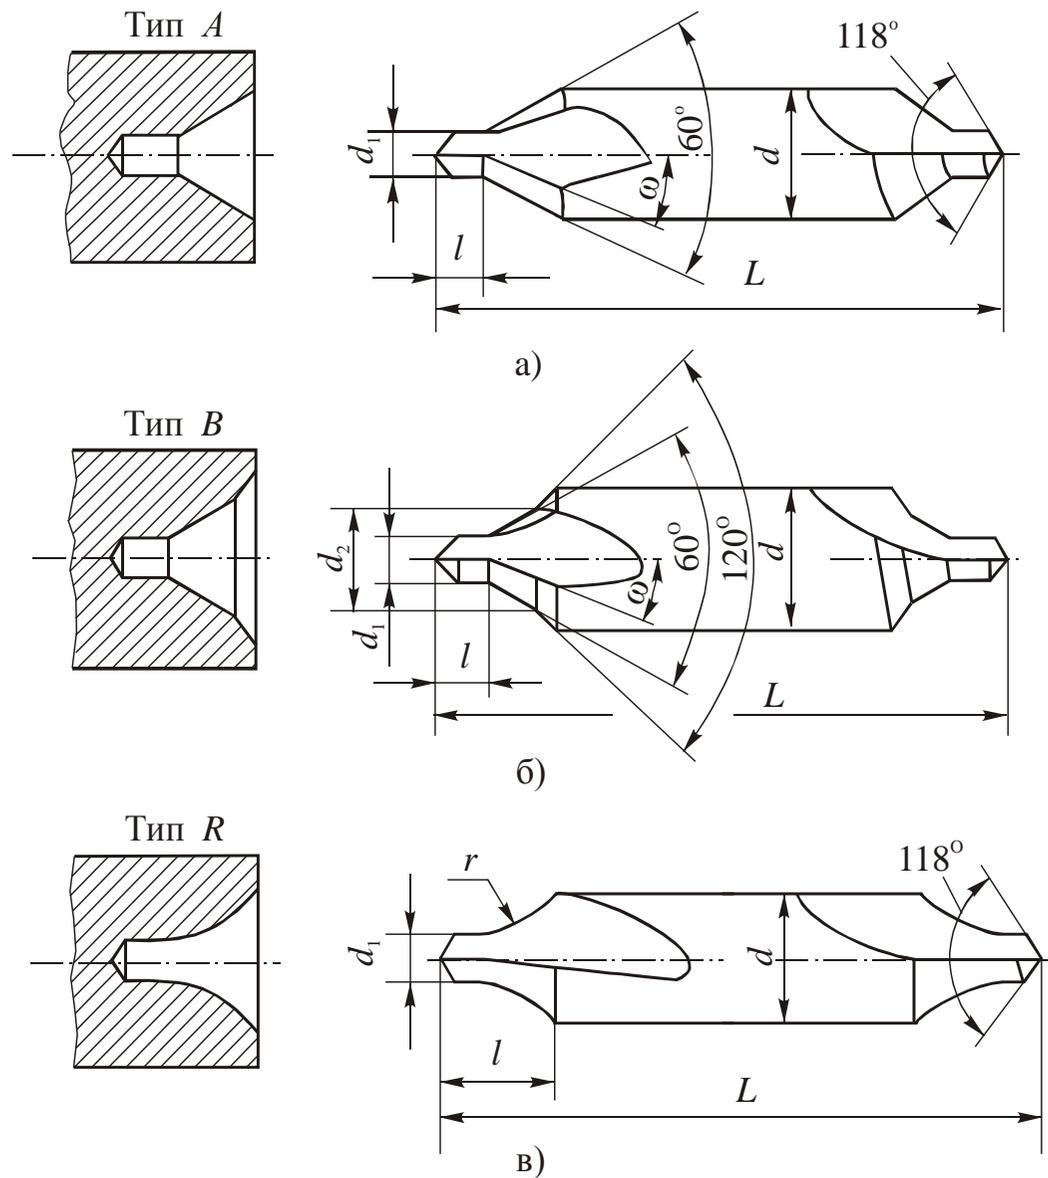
Центровочные сверла-зенковки и получаемые ими типы отверстий: а – без предохранительной фаски; б – с предохранительной фаской; в – радиусное
